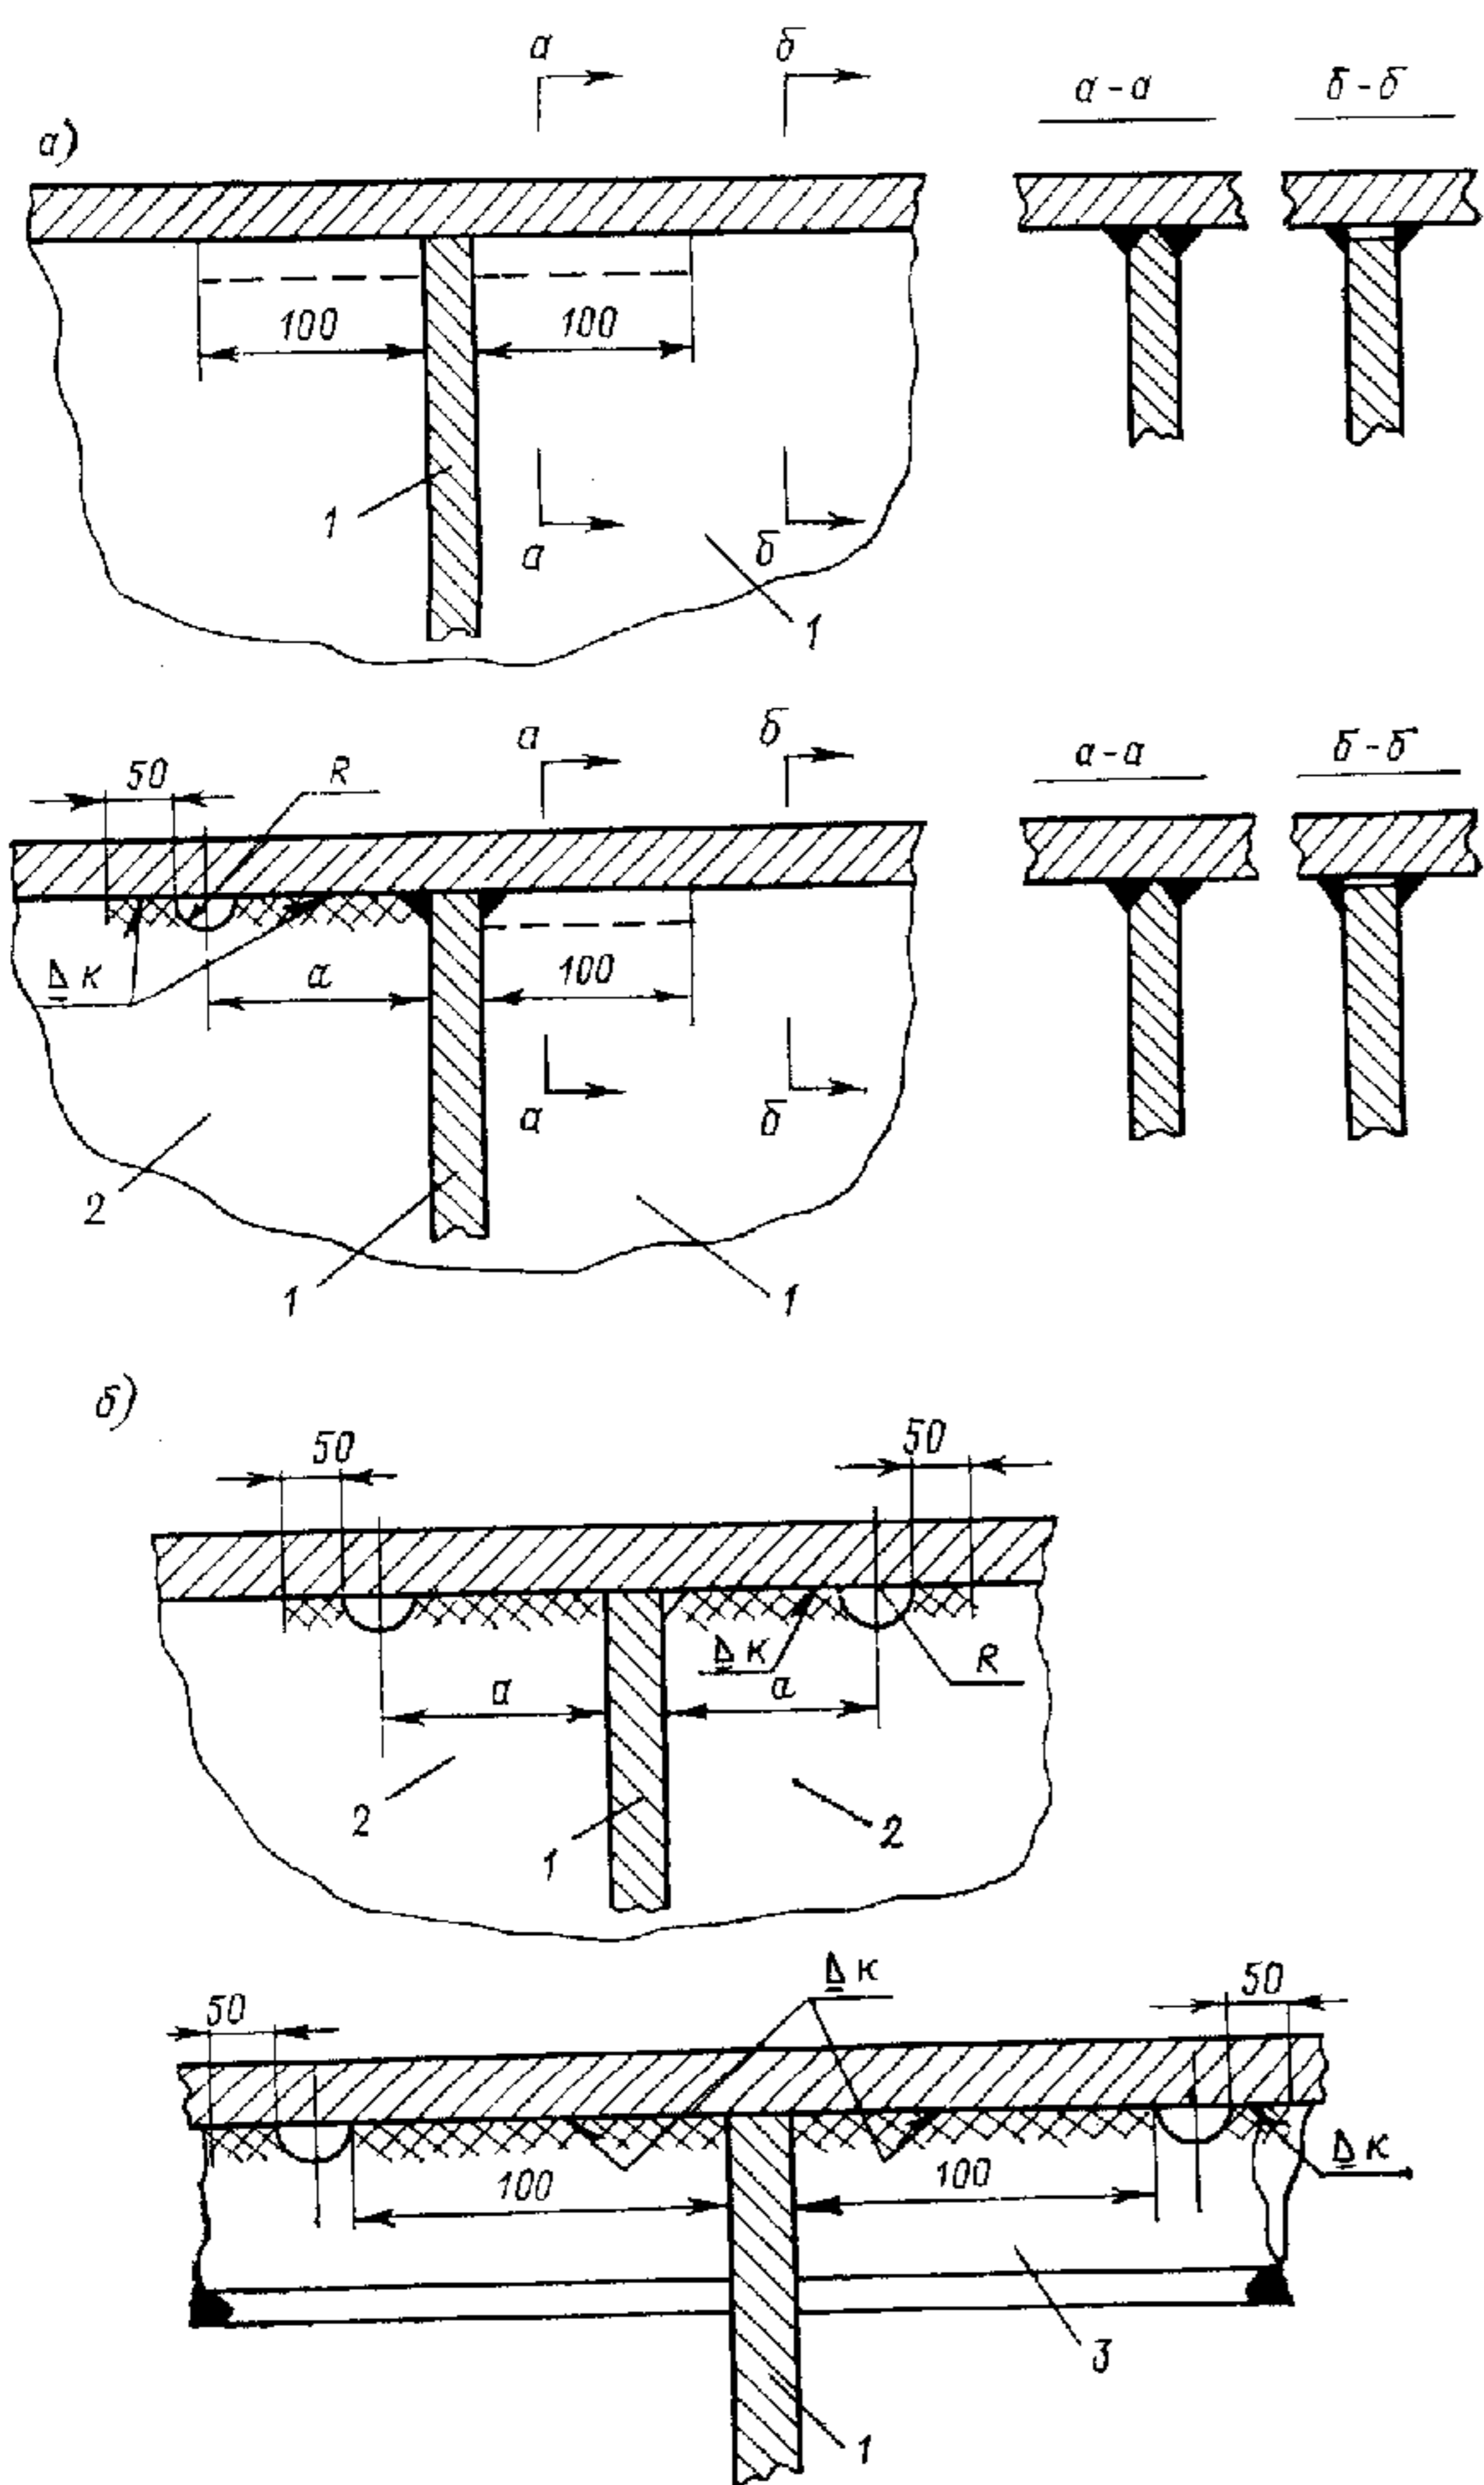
Перемычки в местах прохода балок основного набора через стенки непроницаемых конструкций:
